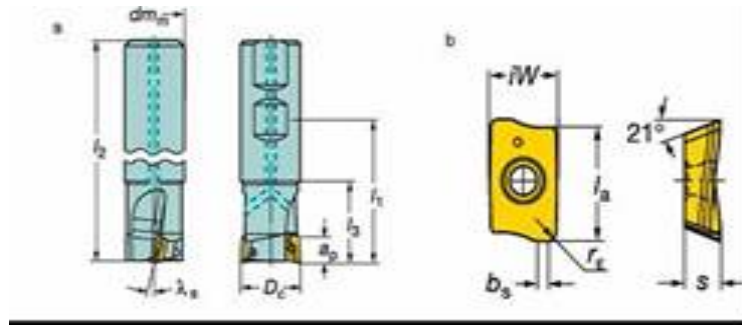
8a) fraise coromill 390 - 8b) détails plaquette
